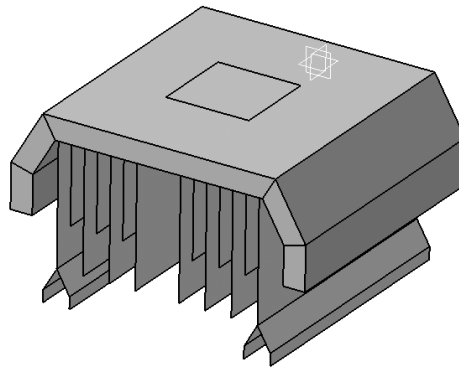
Desenho mecânico do dissipador 11-k751-07.
